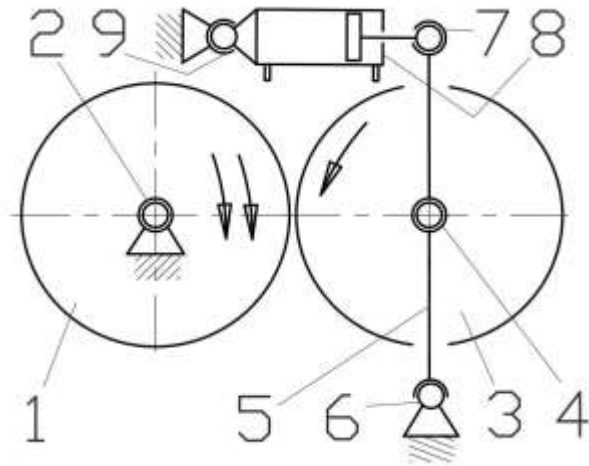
Схема двухвалкової дробарки.
